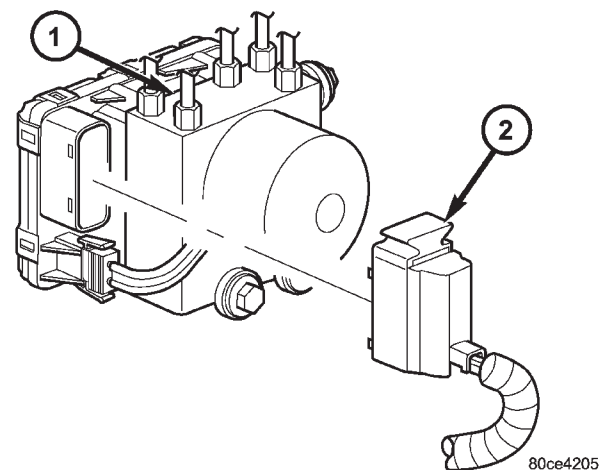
MECANISMO DE DESENGANCHE DE CONECTOR DE MAZO DEL CAB
